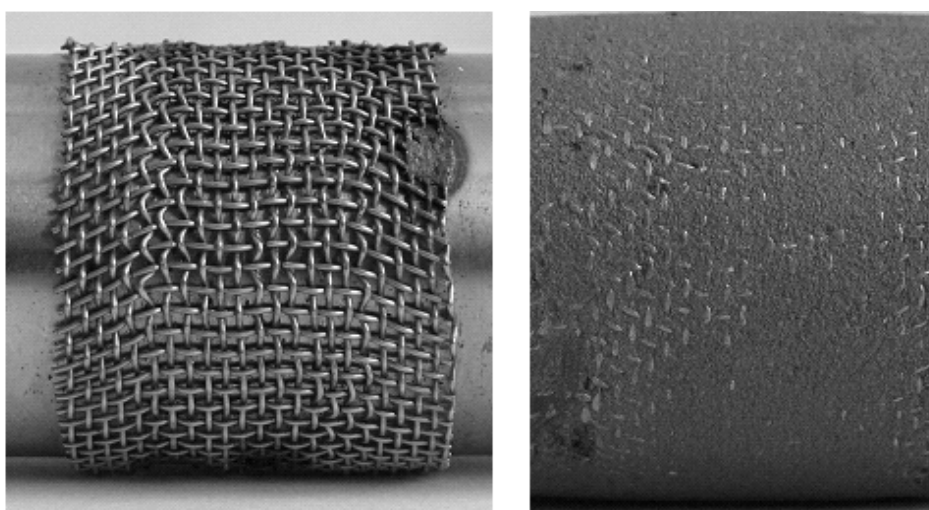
Прихватка стальной сетки на цилиндрическую деталь контактной сваркой и заполнение ячеек сетки металлополимерным материалом
